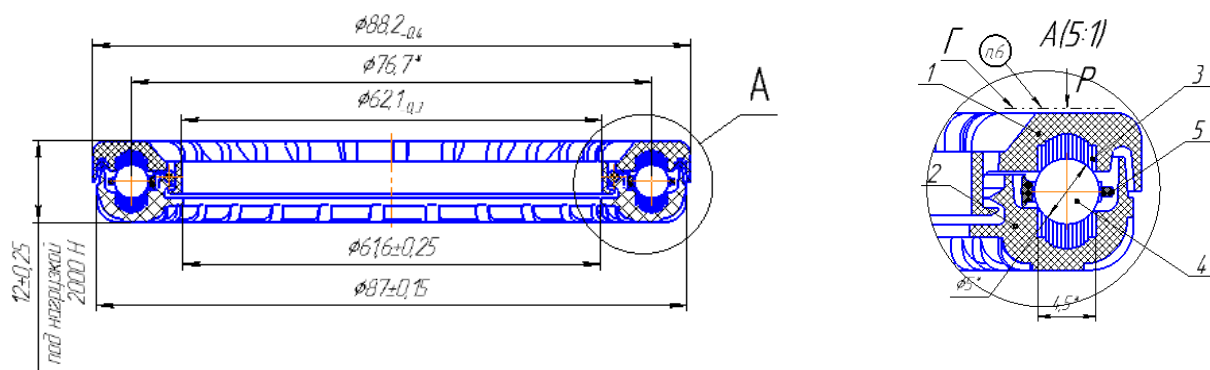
Конструкция подшипника 1118-2902840.
